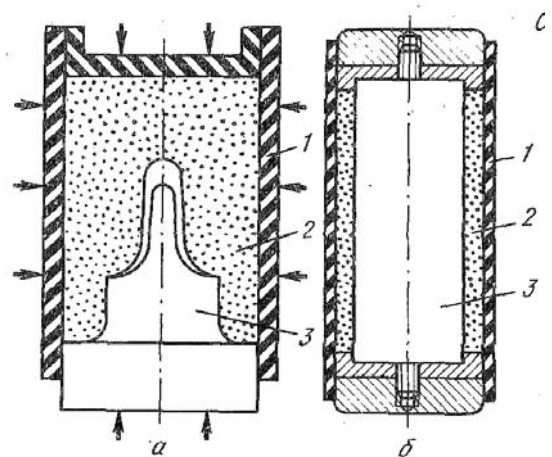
Схема гидродинамического прессования деталей сложной формы: а – пресс-формы; б – фильтрующий элемент; 1 – резиновая оболочка; 2 – порошок; 3 – оправка
